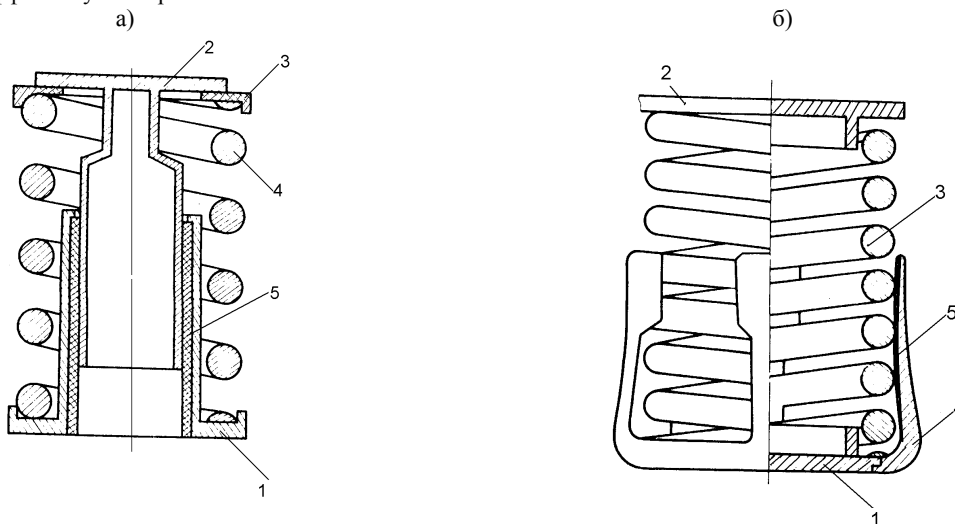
Общий вид виброизолирующего устройства подвески сиденья с демпфером сухого трения: а) втулочного типа, б) с лепестками
